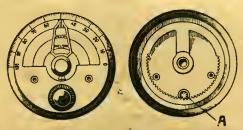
Наружный и внутренний вид ручки верньера с двумя зубчатками. Направо видно колесо с большим вырезом и внутренней зубчатой нарезкой.
